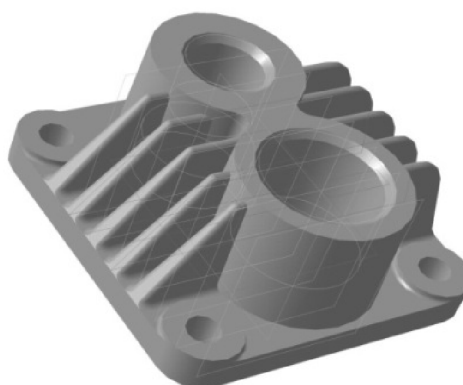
Тривимірною моделлю деталі «Корпус 21.10»
